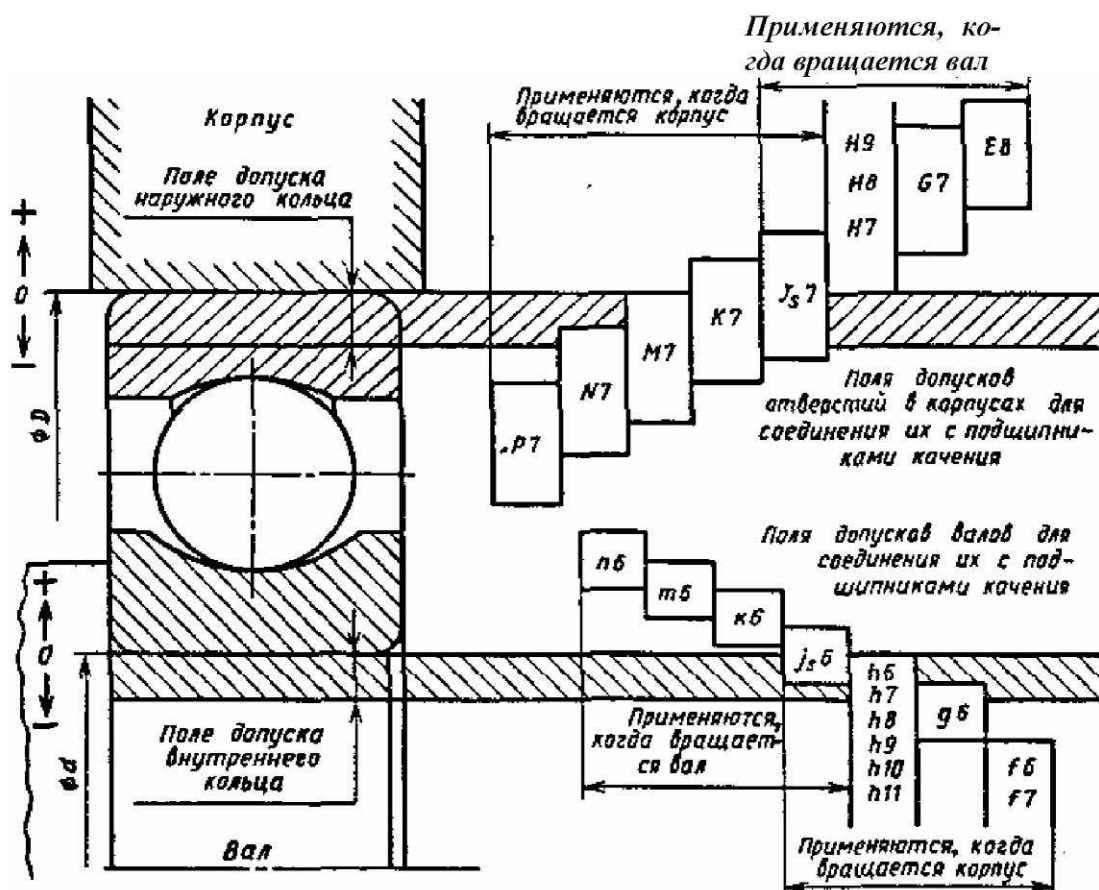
Расположения полей допусков колец подшипника, диаметра вала и корпусного отверстия
